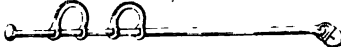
Barre du Gouvernail avec son crapeau sur la tamisaille.
